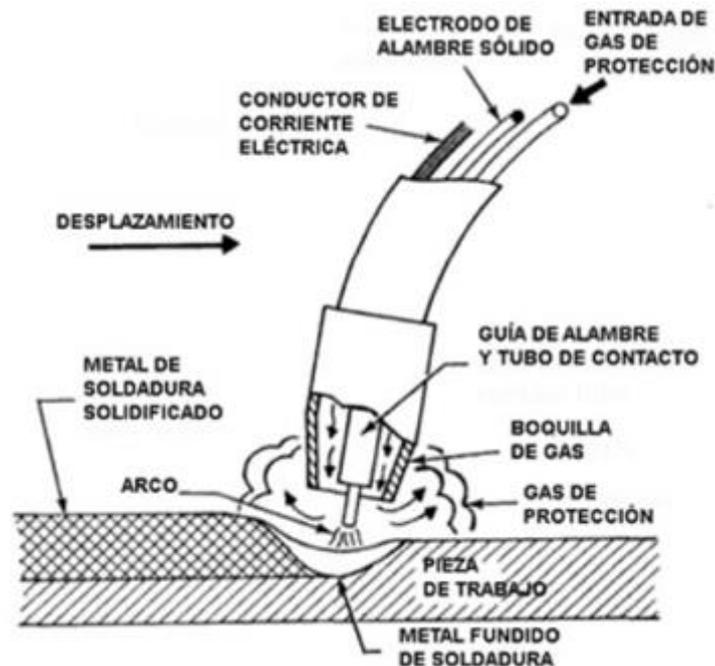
Esquema de soldadura MIG/MAG. [5]
